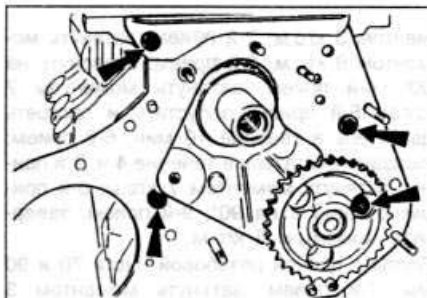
Стрелками показаны болты крепления проставки крышки привода распределительного вала
